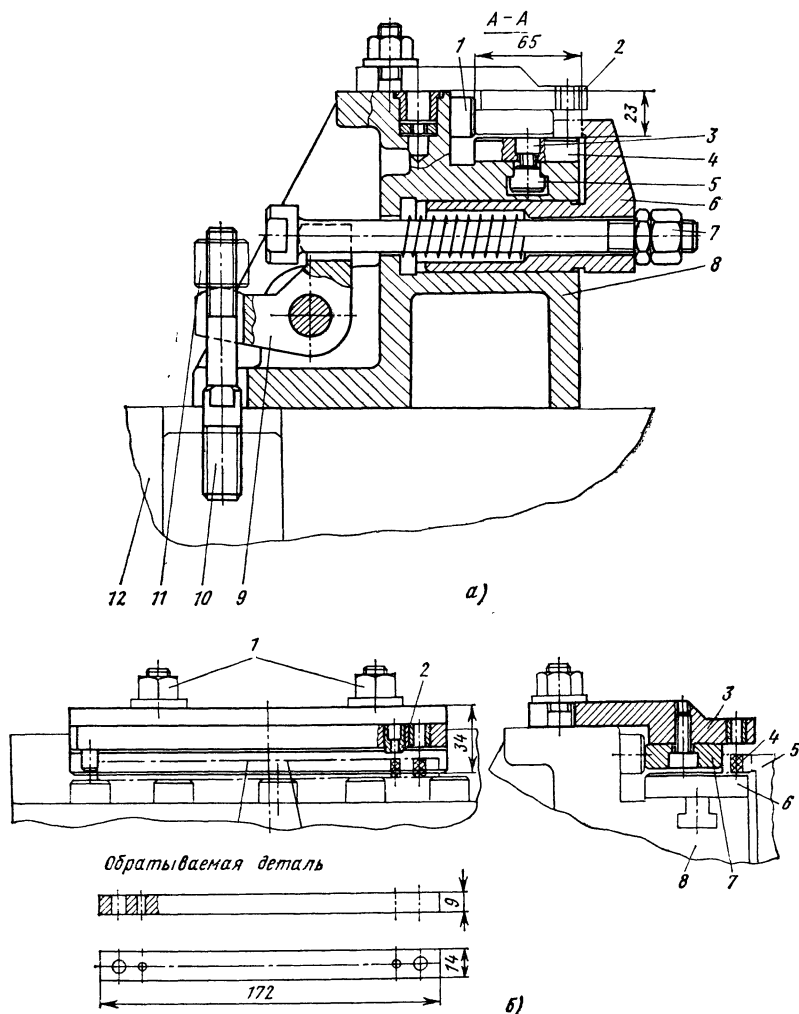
Переналаживаемый кондуктор для сверления отверстий в планках на радиально-сверлильных станках
